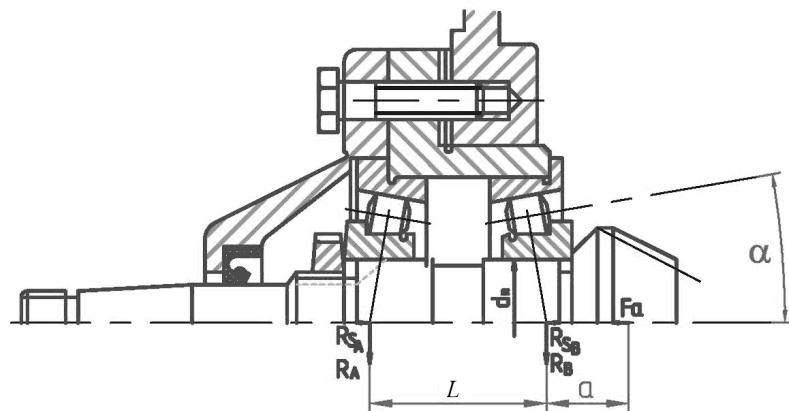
Пример установки вала на конических роликоподшипниках «врастяжку»
